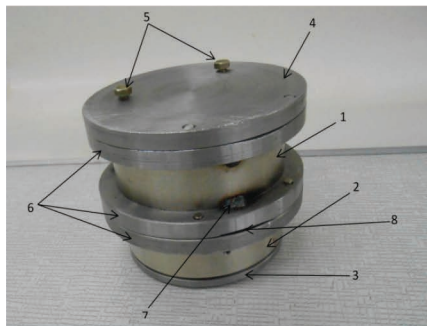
Кювета двойного винтового дожатия (общий вид в сборе). 1. Нижняя часть корпуса (труба и 2 фланца со штифтовыми отверстиями). 2. Верхняя часть корпуса (труба и 1 фланец с отверстиями). 3. Верхняя крышка со ступенчатой вставкой. 4. Нижняя крышка с винтами и отверстиями для трубок. 5. Винты для трубок с винтовыми отверстиями в нижней крышке. 6. Фланцы (сваренные с кольцами трубы ступенчатые шайбы со штифтами и отверстиями для точного соединения частей корпуса). 7. Точка соединения фланца и нижней части корпуса (сварка). 8. Линия соединения «штампа» и «контрштампа».
